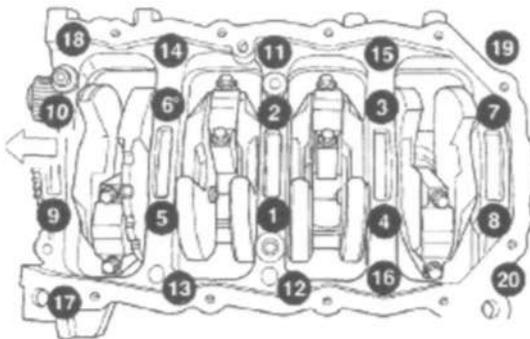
Порядок затяжки болтов крышек коренных подшипников/основания
